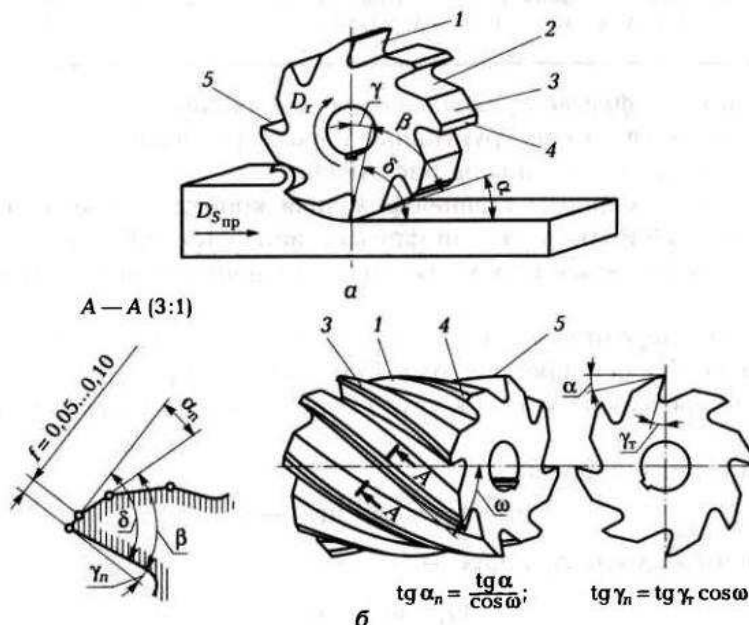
Конструктивные и геометрические параметры цилиндрических фрез с прямыми (а) и винтовыми (б) зубьями:
